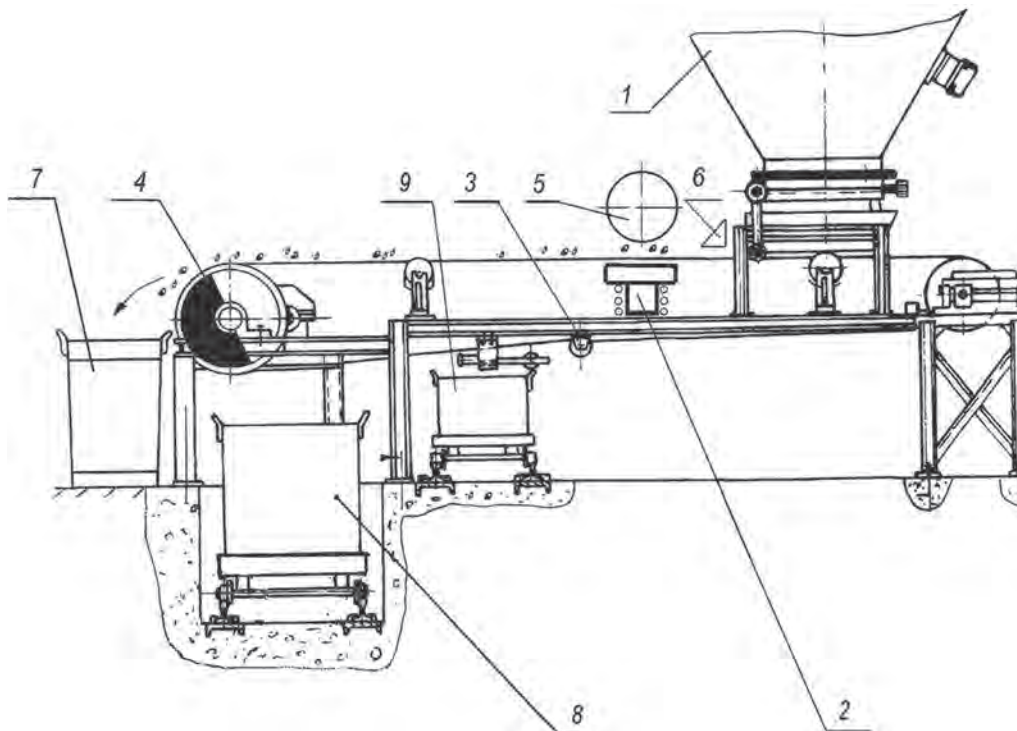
Устройство магнитной сепарации: 1 – бункер; 2,5 – встряхиватель; 3 – транспортер; 4 – магнитный сепаратор; 6 – щелевой дозатор; 7– 9 – тара
